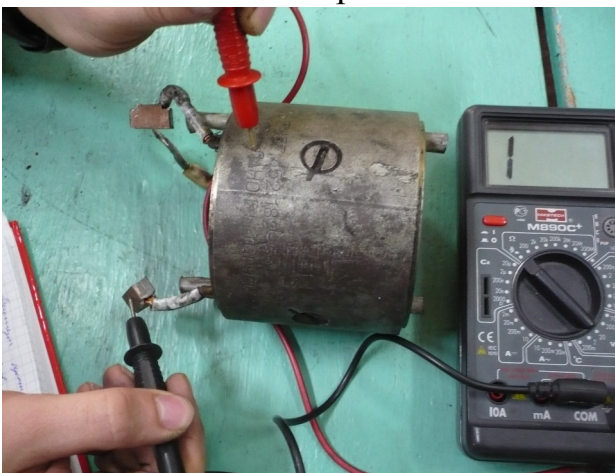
Проверка обмотки статора на замыкание с корпусом
